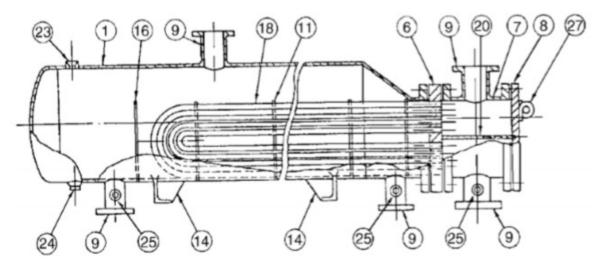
Partes de un intercambiador de calor de carcasa y tubos
